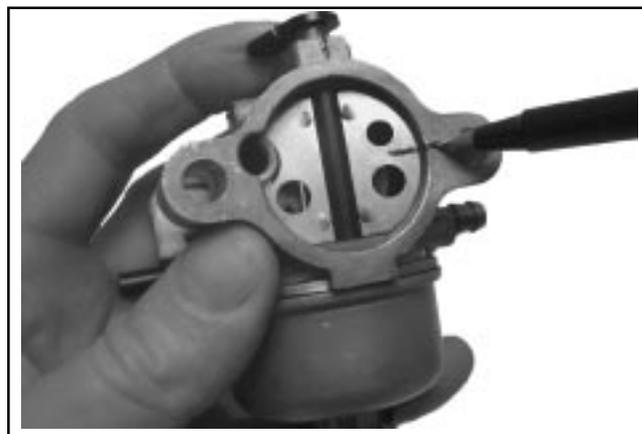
Marquage de la plaque du starter et du corps du carburateur.
